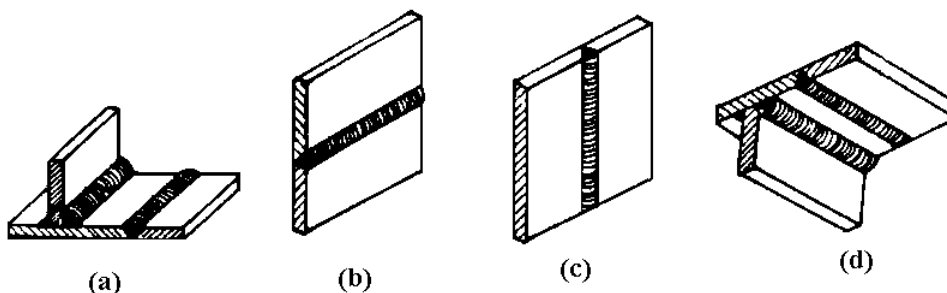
Diferentes posições de soldagem, a) Plana, b) Horizontal, c) Vertical, d) Sobre-cabeça
